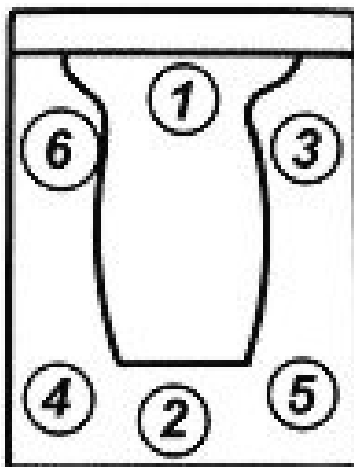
Порядок затяжки болтов крепления головок цилиндров
